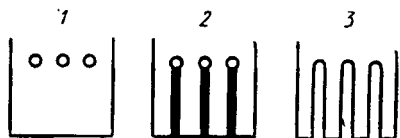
Схема обработки вильчатых хвостов со сверлением отверстий у дна паза:
